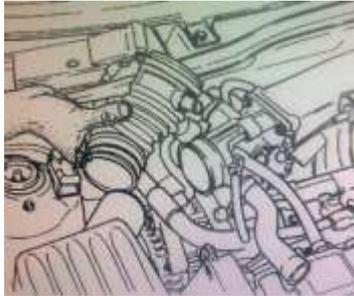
Desmontaje del Ducto de Admisión de Aire
